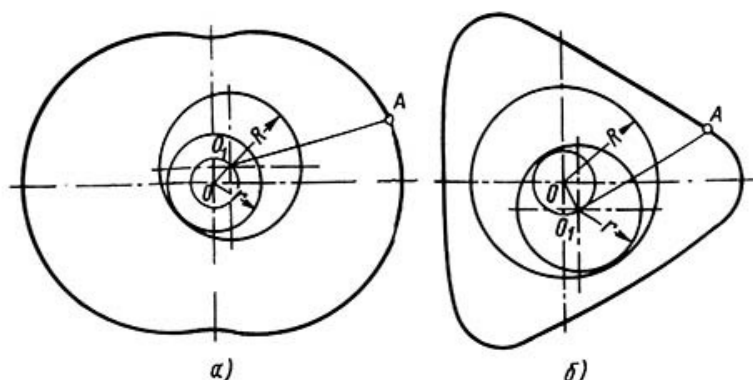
Образование трохоид в роторно-поршневом двигателе:
